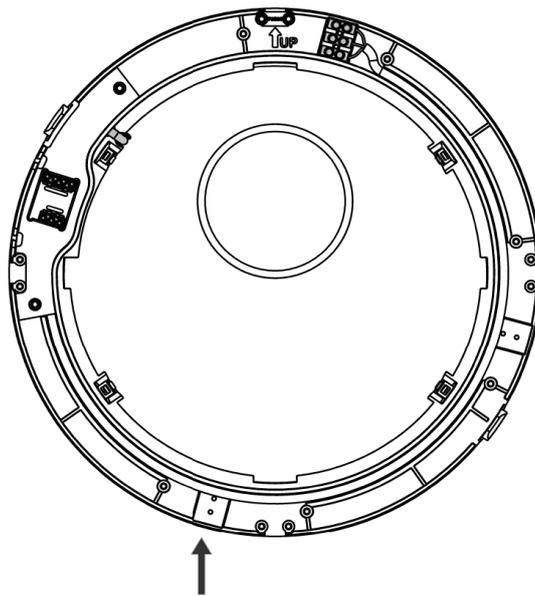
Emplacement de la borne 2 en cas de passage des câbles par le bas
